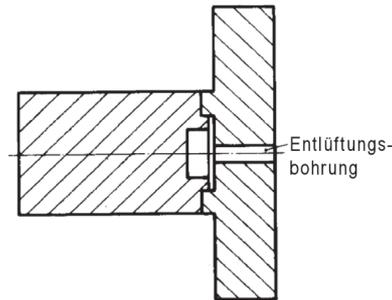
Bauteil mit Bohrung zum Entlüften des Hohlraums.
